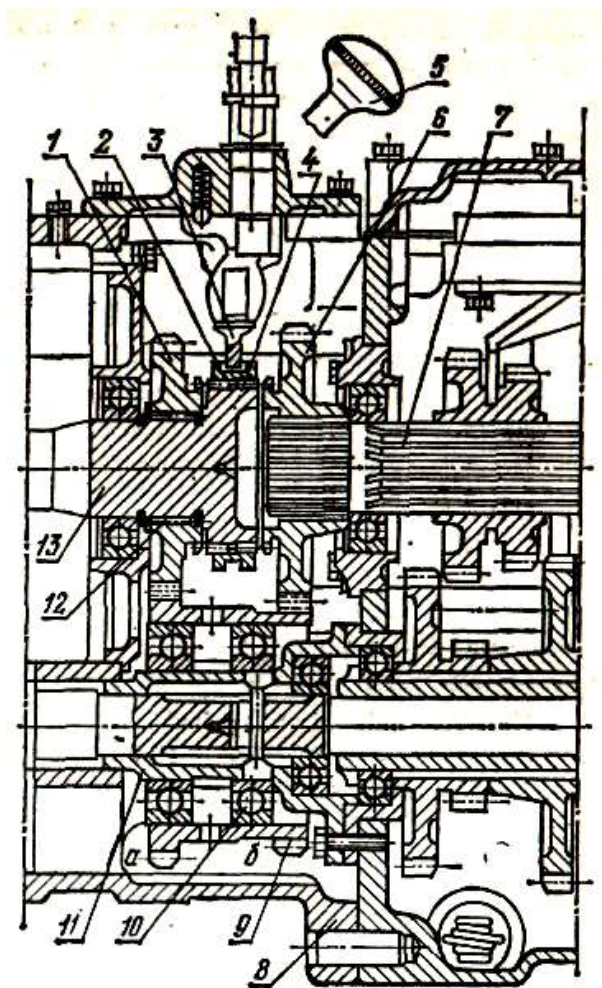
Понижающий редуктор коробки передач тракторов Беларус 80.1
